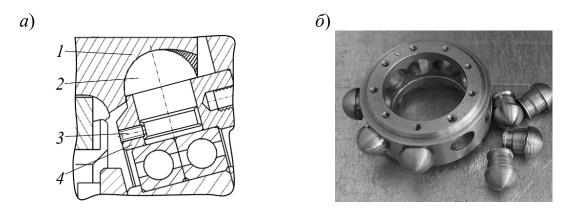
Механизм фиксации ролика: a – схема; δ – детали образца
